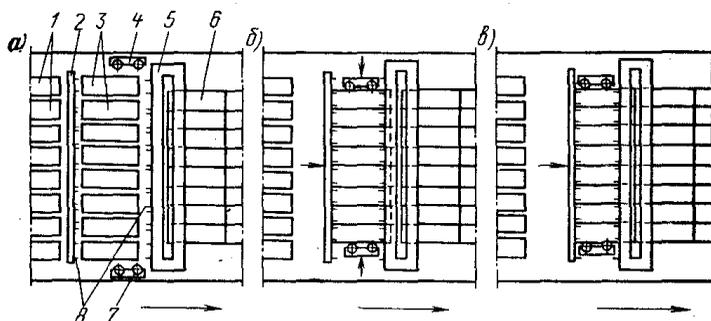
Схема механизированной сборки крупногабаритных полотнищ без прихваток:
